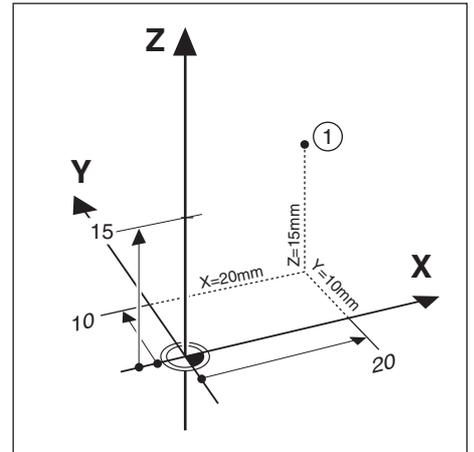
Posición ① del ejemplo "posiciones absolutas de pieza"
